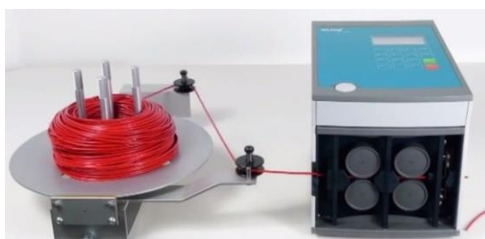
Общий вид автомата мерной резки ПВХ трубок модели LC100SL.
